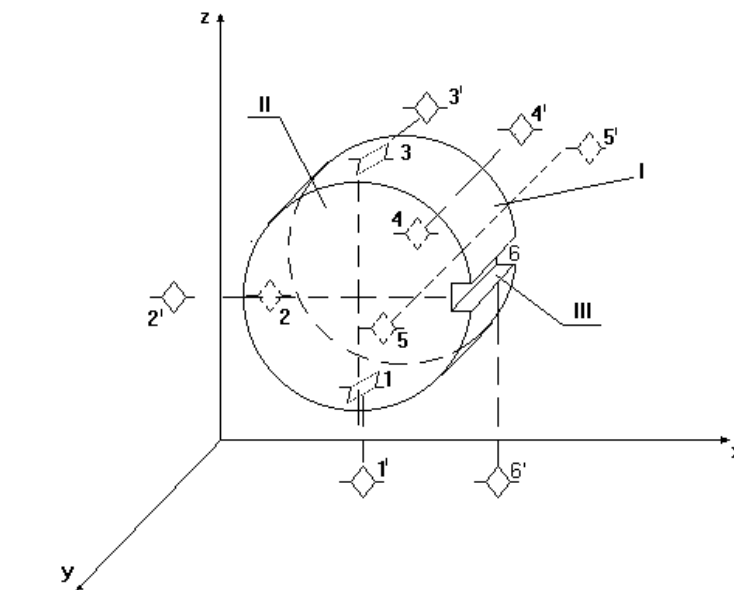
Приклад розташування опорних точок на дисковій заготовці з комплектом баз I, V, III'
